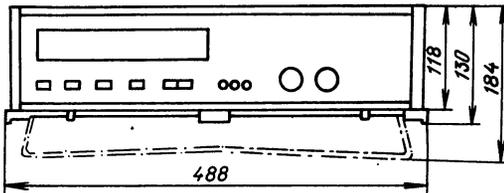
Габаритный чертеж прибора типа ЦШ302
